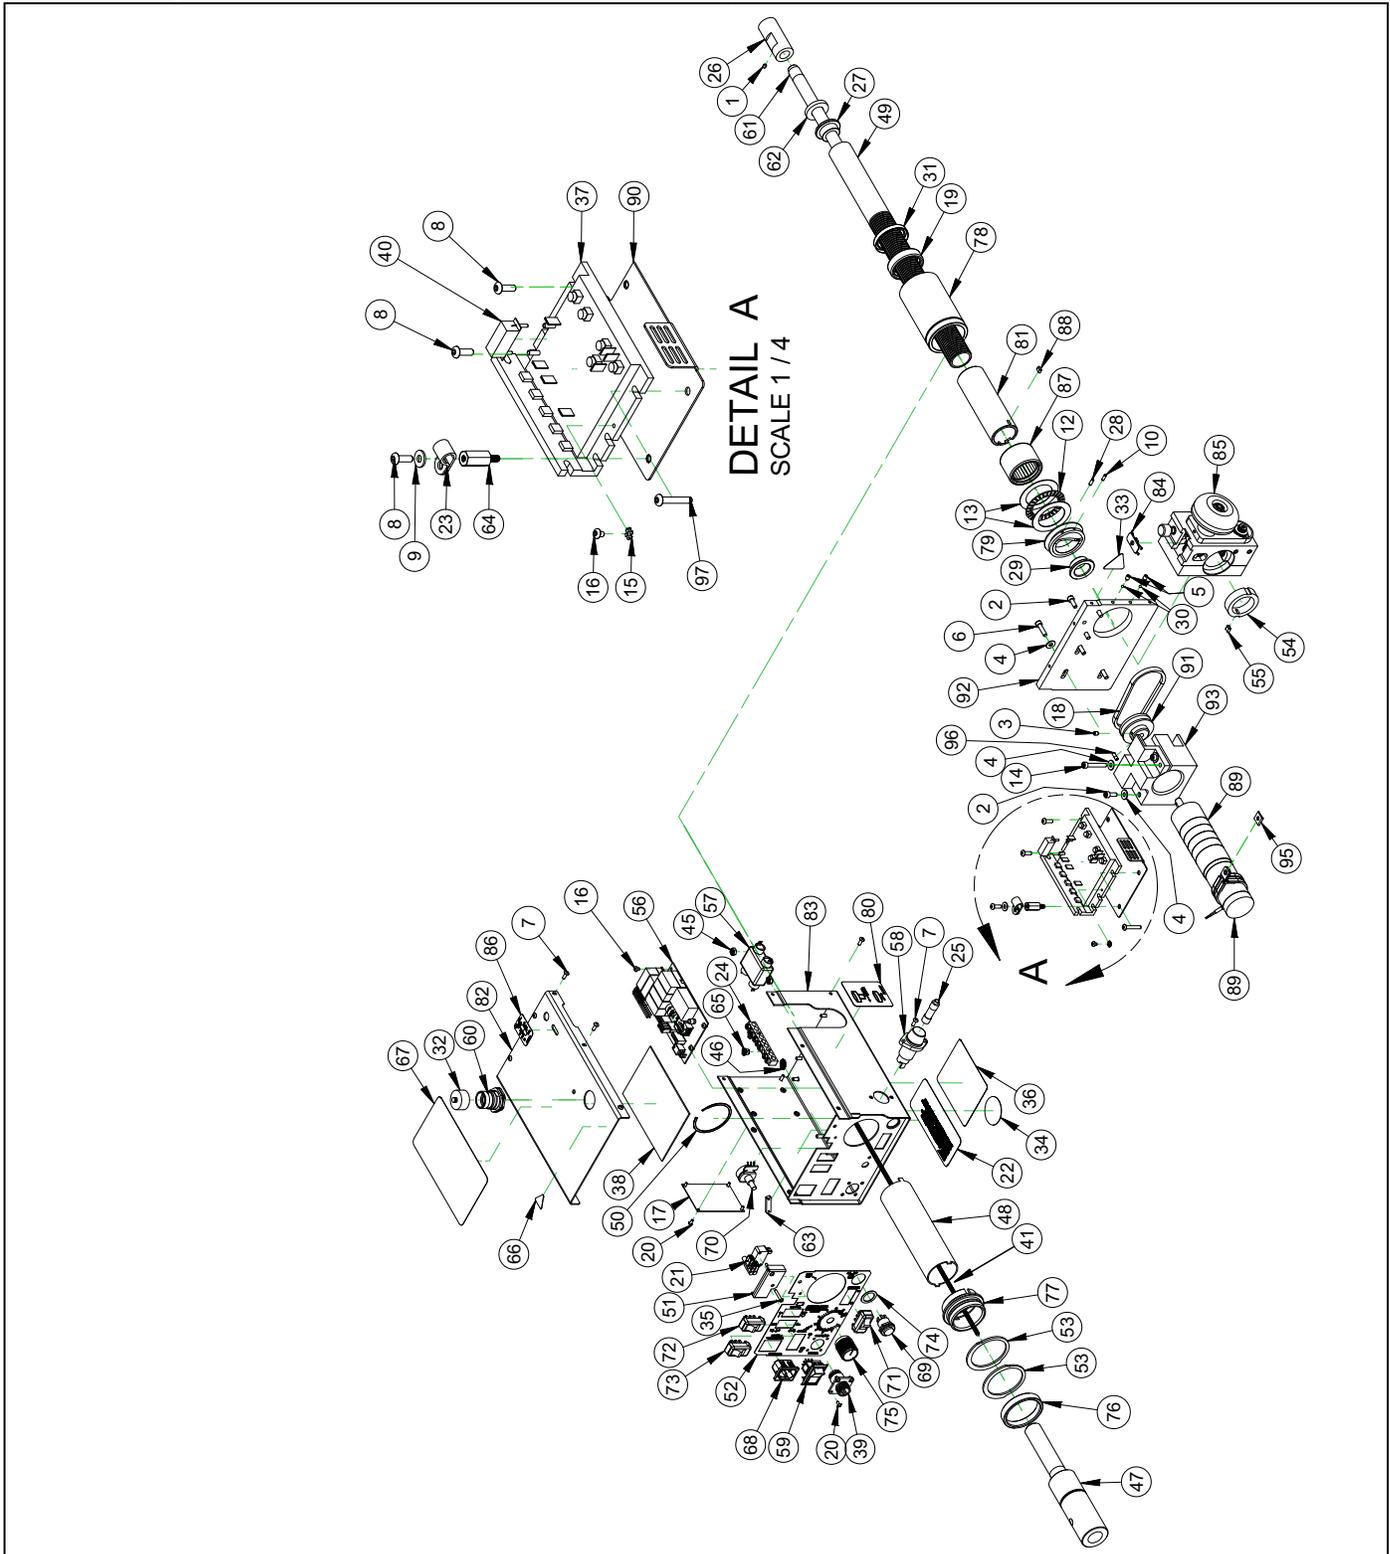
CONJUNTO DEL CABEZAL DE SOLDADURA (N/P 103268)
